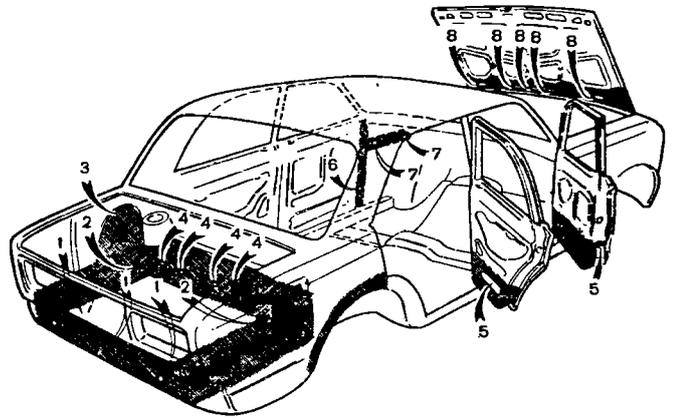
Скрытые полости кузова (вид справа): 1 - нижней поперечины задка; 2 - лонжеронов пола задка; 3 - между крыльями и арками задних колес; 4 - поперечины заднего пола; 5 - карманов дверей; 6 - передних стоек; 7 - соединителей боковины и щитка передка; 8 - карманов капота
